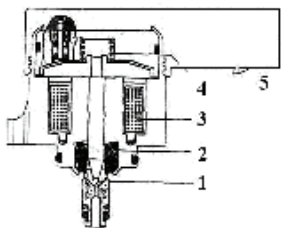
Исполнительный электромагнитный клапан регулятора давления:
